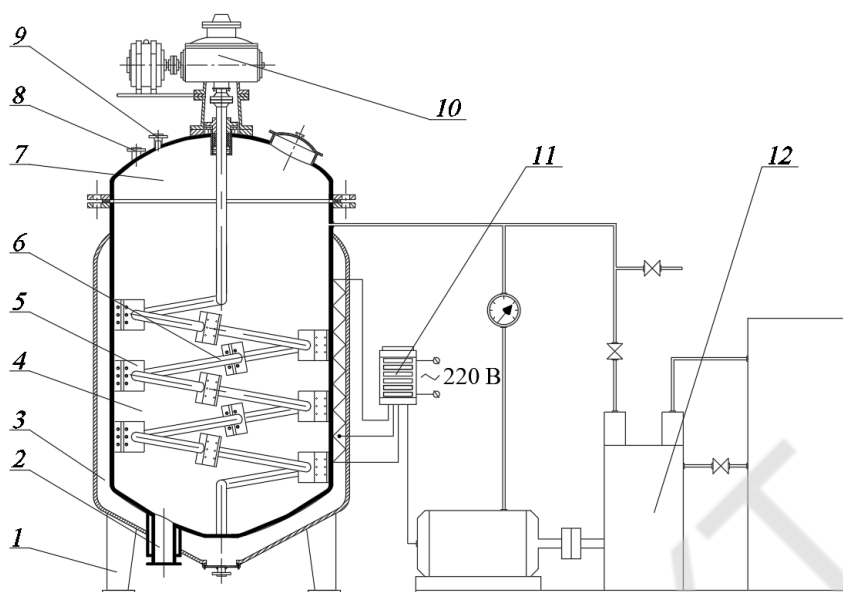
Установка для уварювання овочевої сировини під вакуумом при постійному перемішуванні: 1 – опори; 2 – патрубок для зливання готового продукту; 3 – парова сорочка; 4 – робоча камера апарату; 5 – скребок перемішуючого пристрою; 6 – вал мішалки; 7 – кришка апарату; 8 – патрубок для відведення вологи; 9 – патрубок для подачі сировини; 10 – електродвигун; 11 – блок керування робочими процесами апарату; 12 – система вакуумування апарату.
